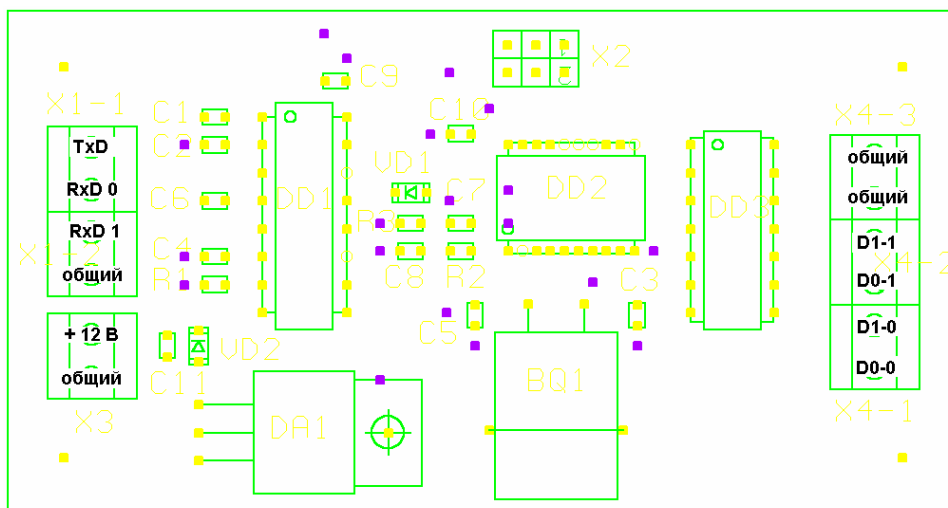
внешний вид конвертора «СКД ШК-01».
